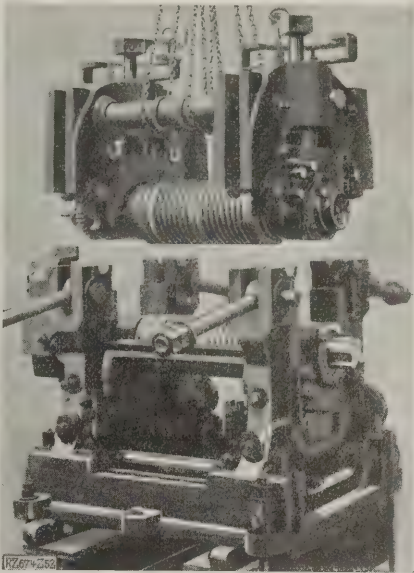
Walzgerüst zur Vorstraße nach Abb. 49, Deckel und Oberwalze abgehoben.
